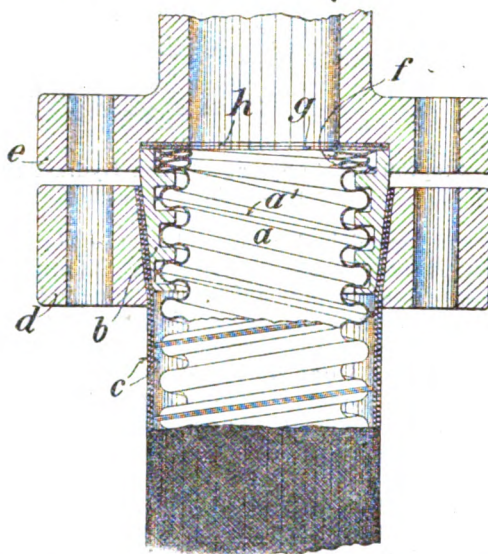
Endverbindung für geschweißte Metallschläuche.
